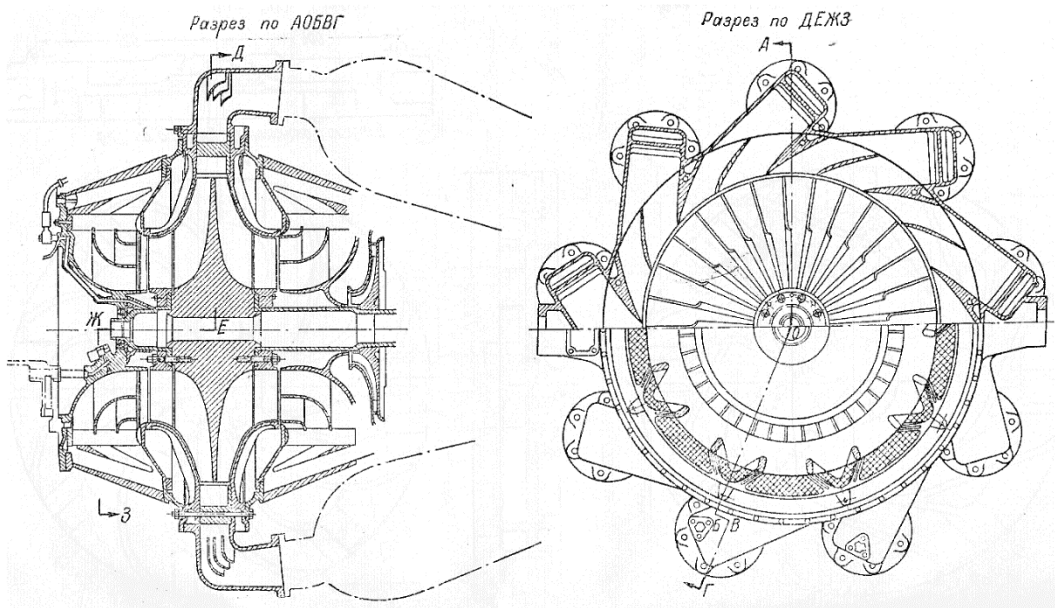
Двухпоточный одноступенчатый центробежный компрессор турбореактивного двигателя середины 20 в.
